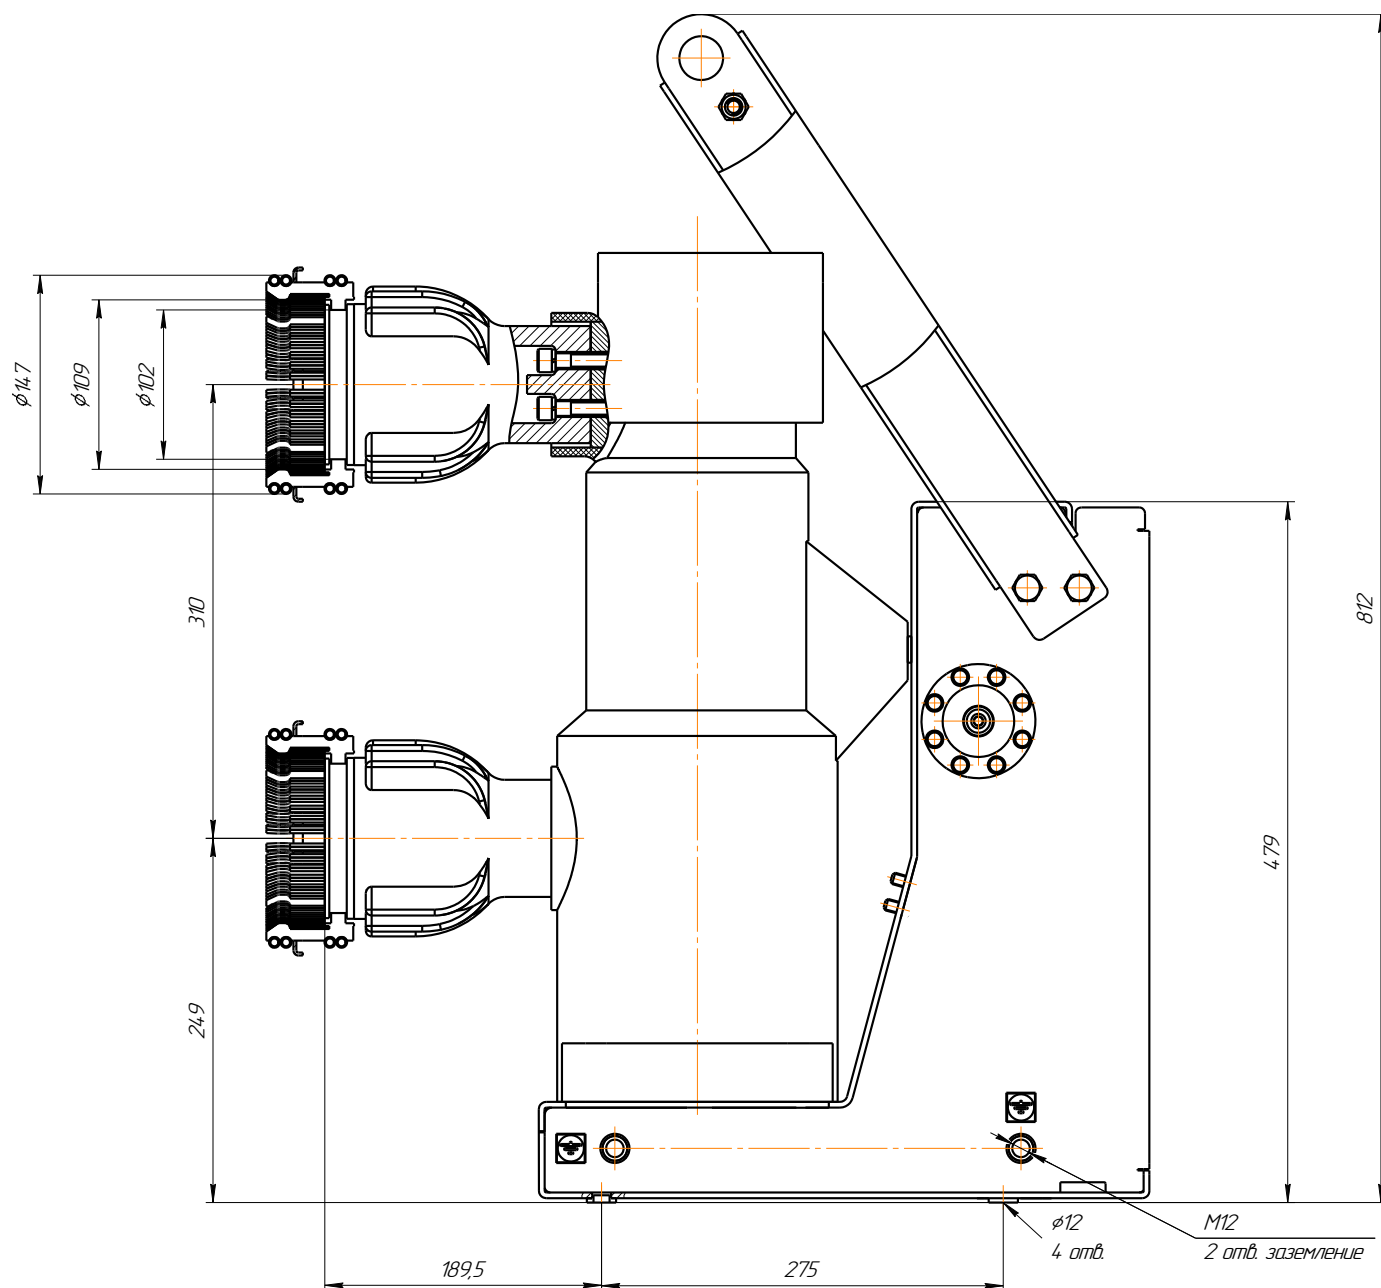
Габаритные и присоединительные размеры выключателя ВБУ-СЭЩ-10-40
